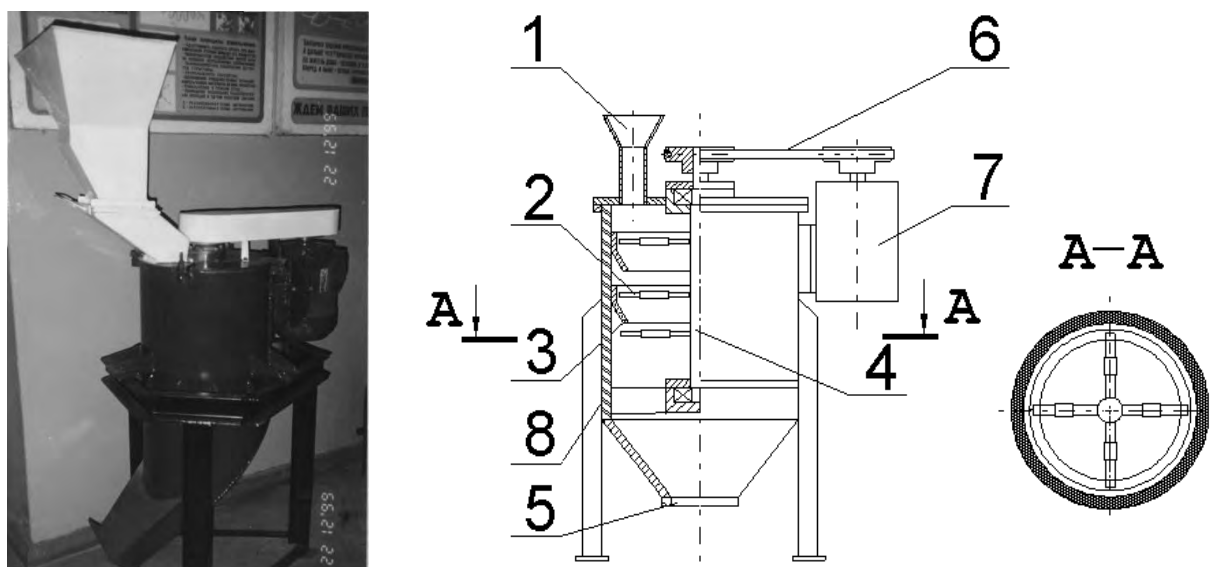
Дробильная установка ударного действия и схема ее конструкции: 1 – загрузочный бункер; 2 – ударные элементы; 3 – отражатель; 4 – вертикальный вал; 5 – выпуск готовой продукции; 6 – ременная передача; 7 – электродвигатель; 8 – корпус
